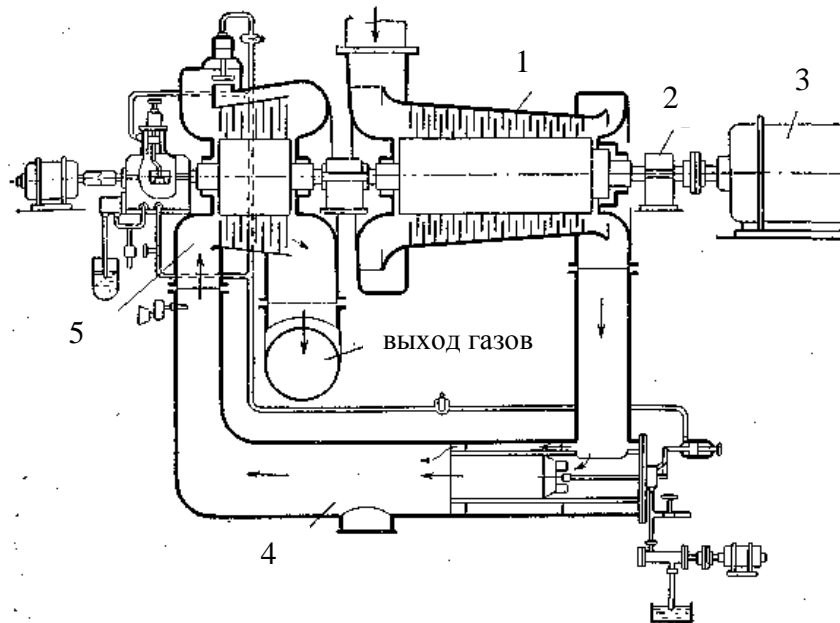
Схема установки осевого компрессора с газовой турбиной
